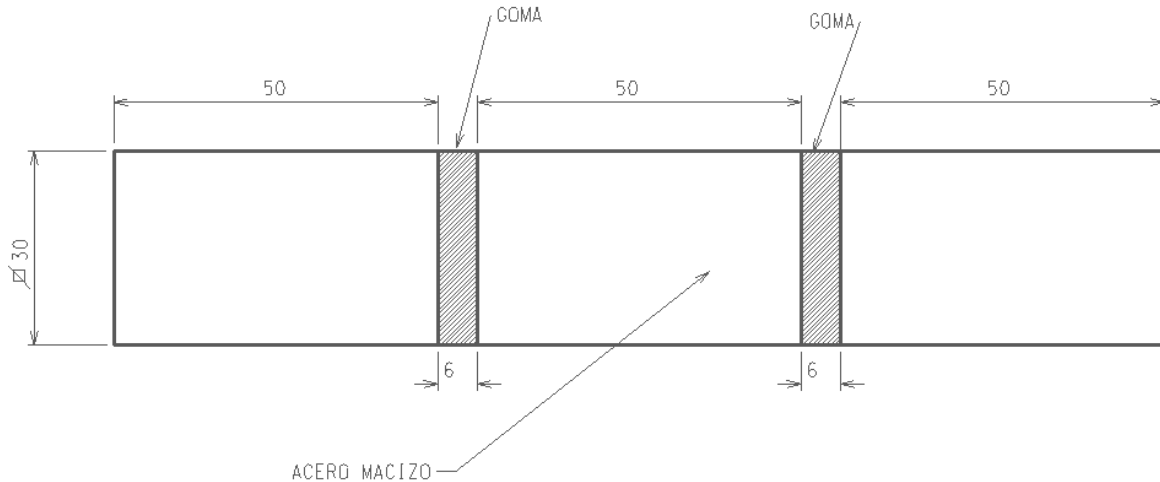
, Dimensiones de probeta para ensayo de corte. (dim. en mm)
